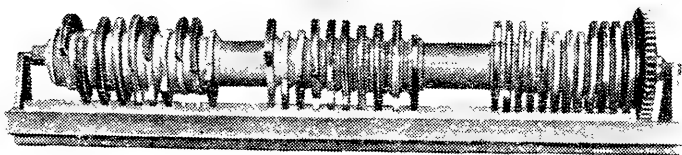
Шаблон для проверки правильности установки шайб по длине кулачкового вала реостатного контроллера ПКГ-320А-2
